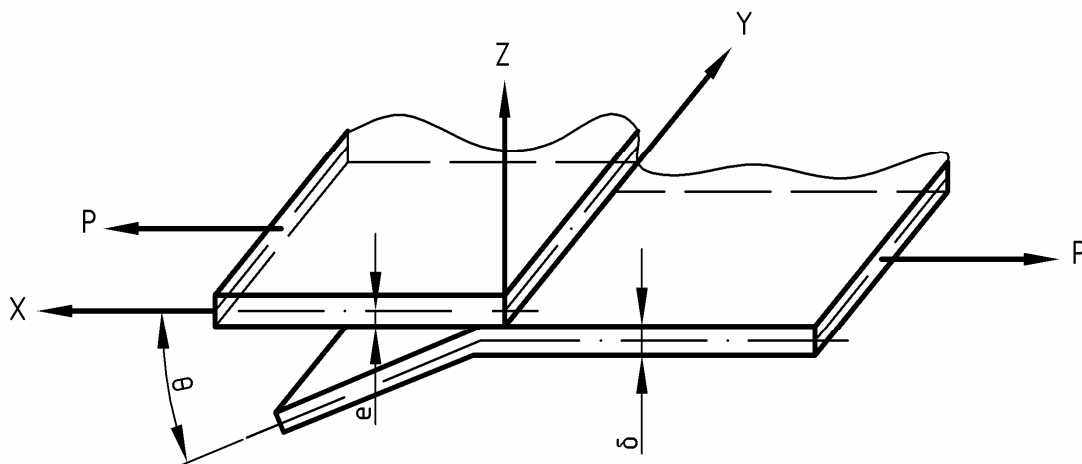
Схема испытаний нахлесточных сварных соединений
